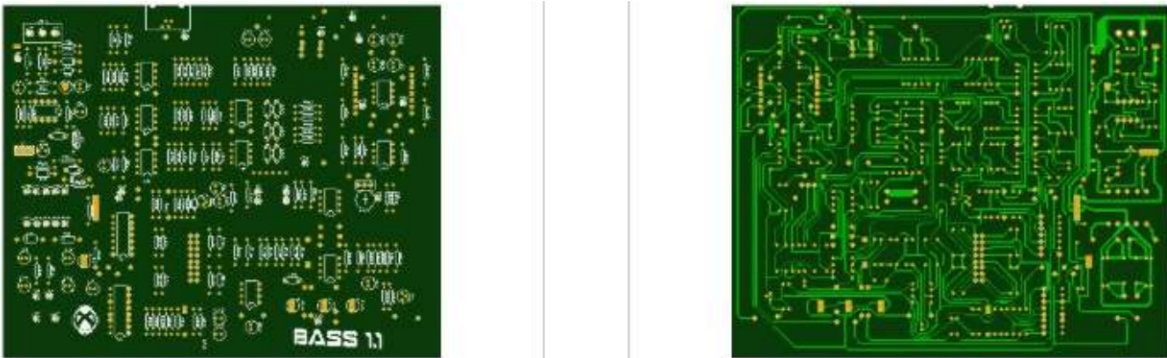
Vista de Gerbers con simulador www.jlcpcb.com
